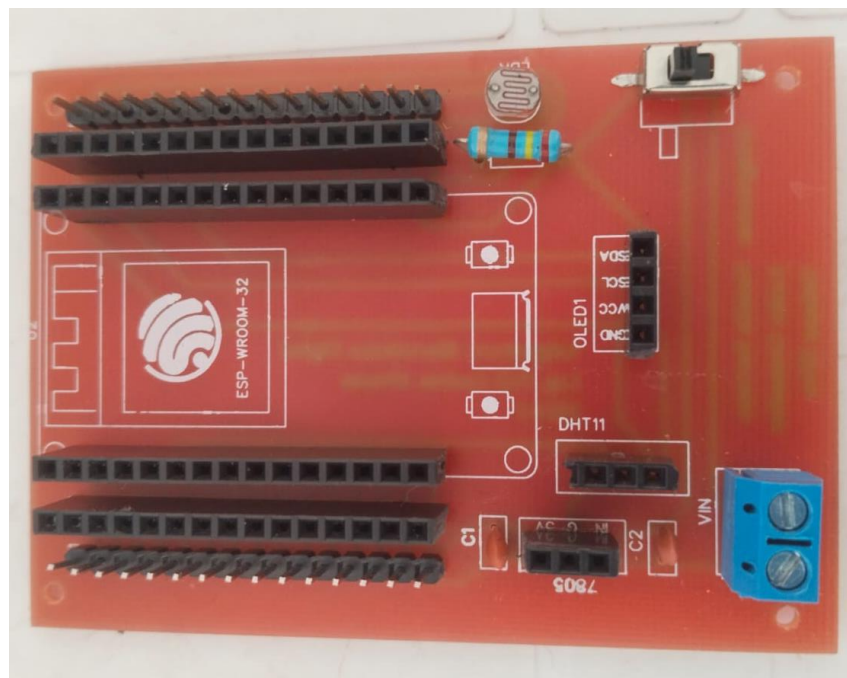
PCB ensamblada con los pines soldados.
